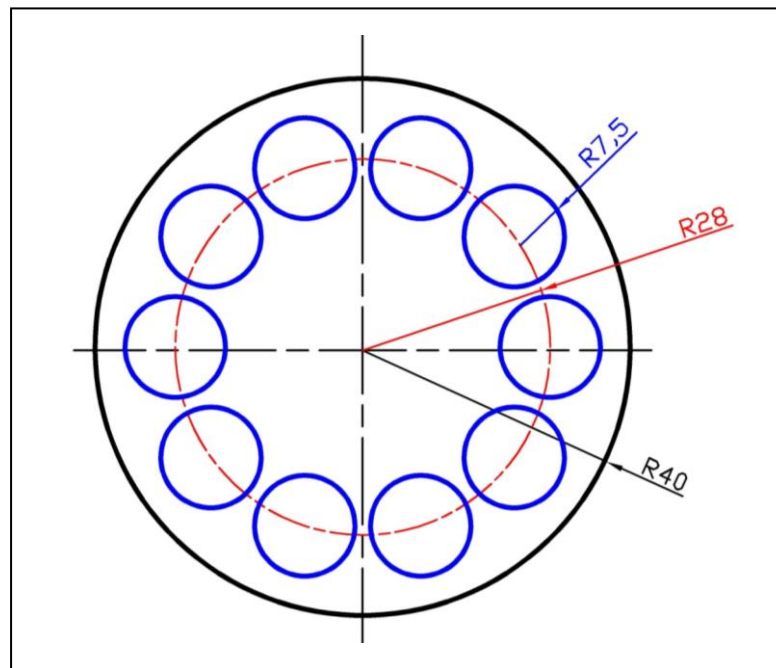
Plan de découpe des éprouvettes de fatigue.
